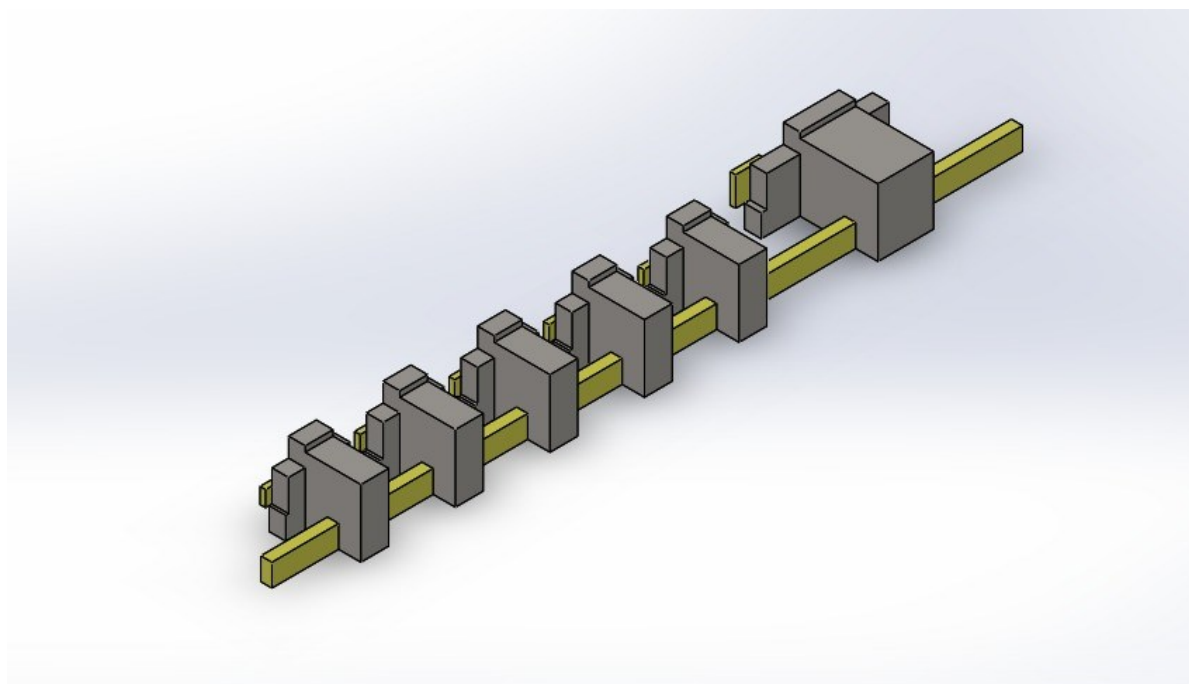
Novo layout da linha de produção com a instalação da estação de brunimento flexível após as máquinas de brunimento precisor. (O AUTOR, 2020).
